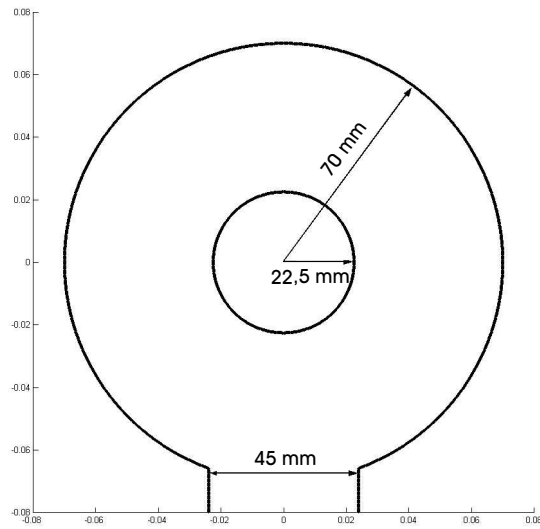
Ejemplo de llenado de un molde: Dimensiones del molde.
